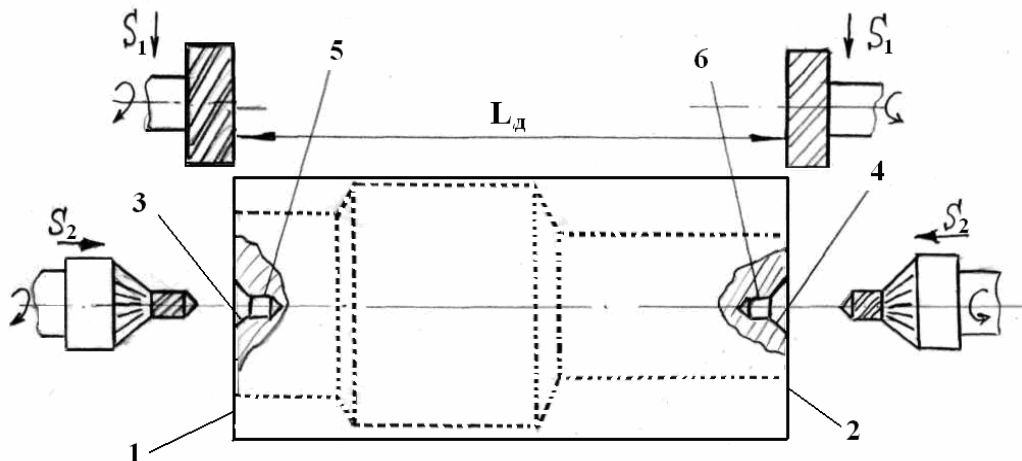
Установка детали на фрезерно-центровальних верстатах (схема)
